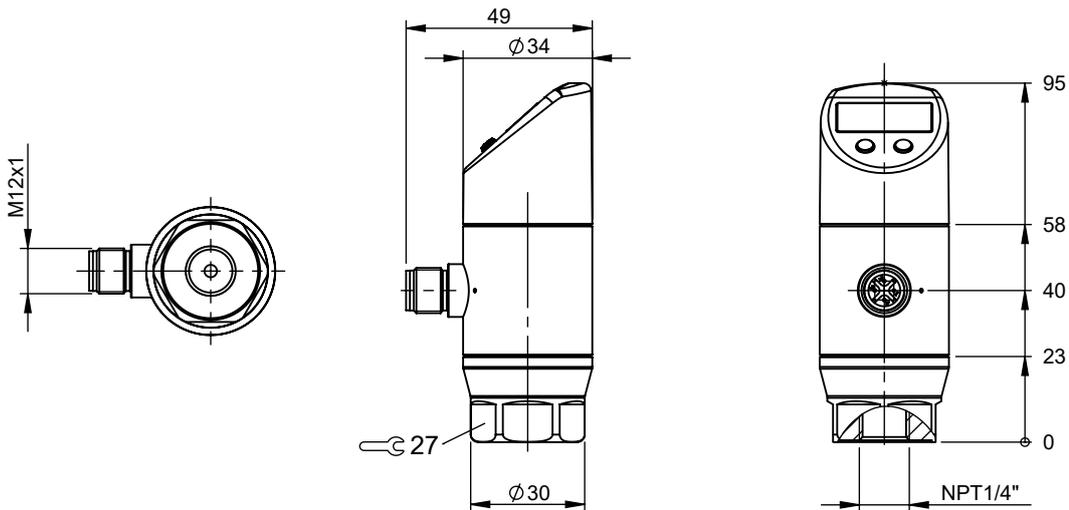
BSP - - - - -GV009-P S2B-S4..., nicht frontbündig, NPT 1/4", Innengewinde, IP67
